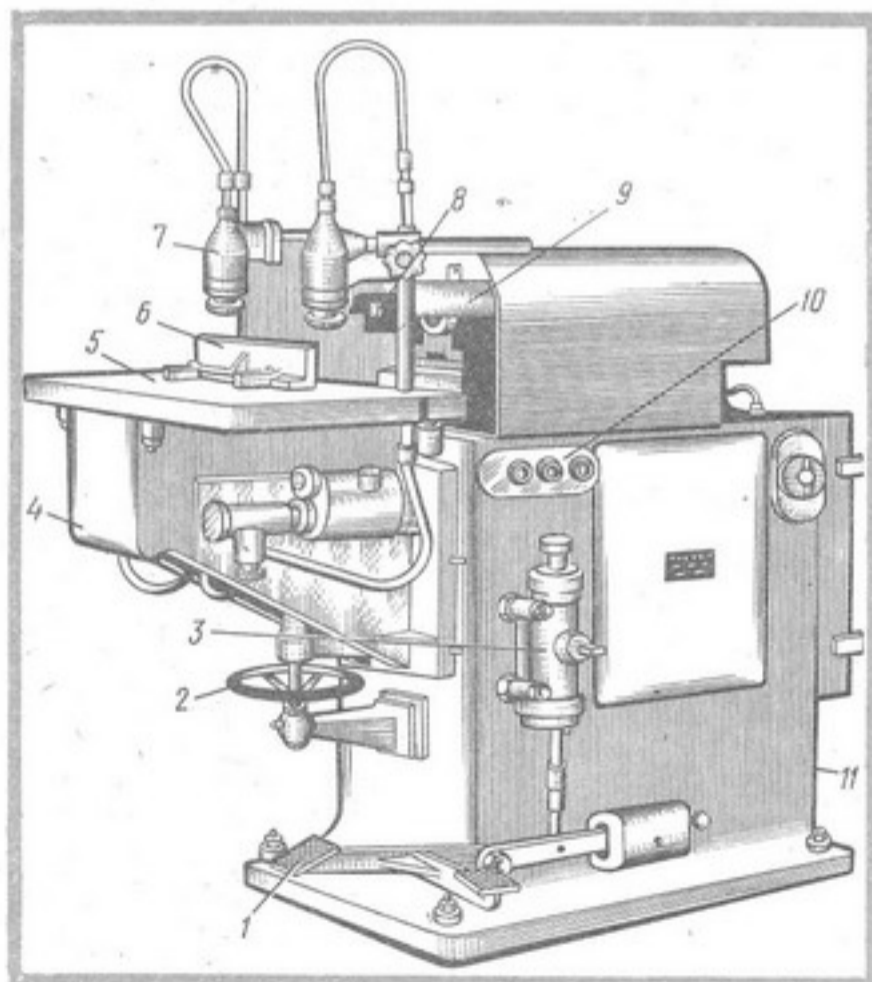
Сверлильно-пазовальный станок СВПА-2:
